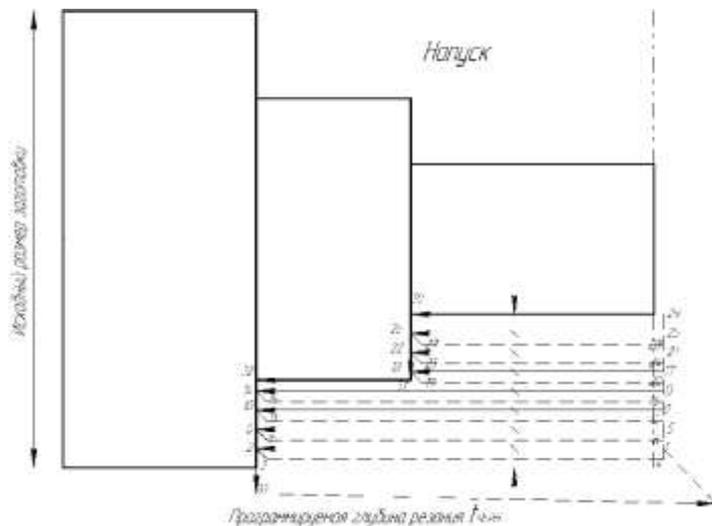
Схема удаления напуска и чернового припуска из полуоткрытой зоны обработки
